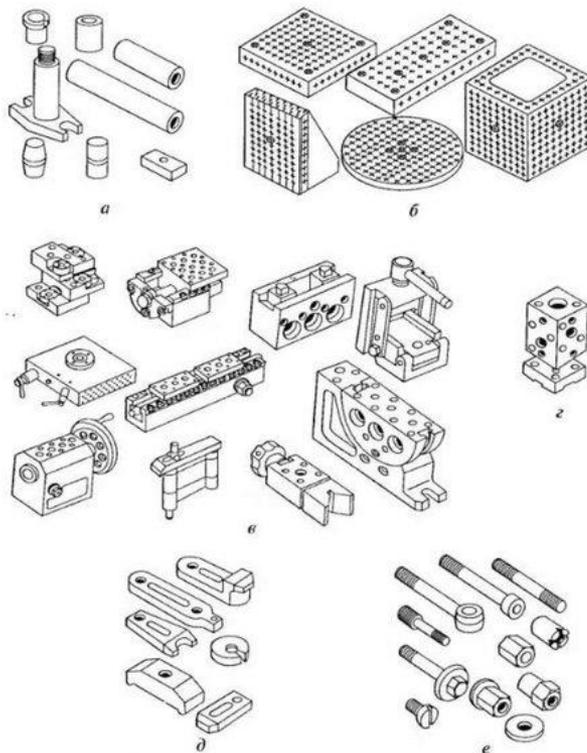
Базовый набор деталей и сборочных единиц универсально-сборных приспособлений:
